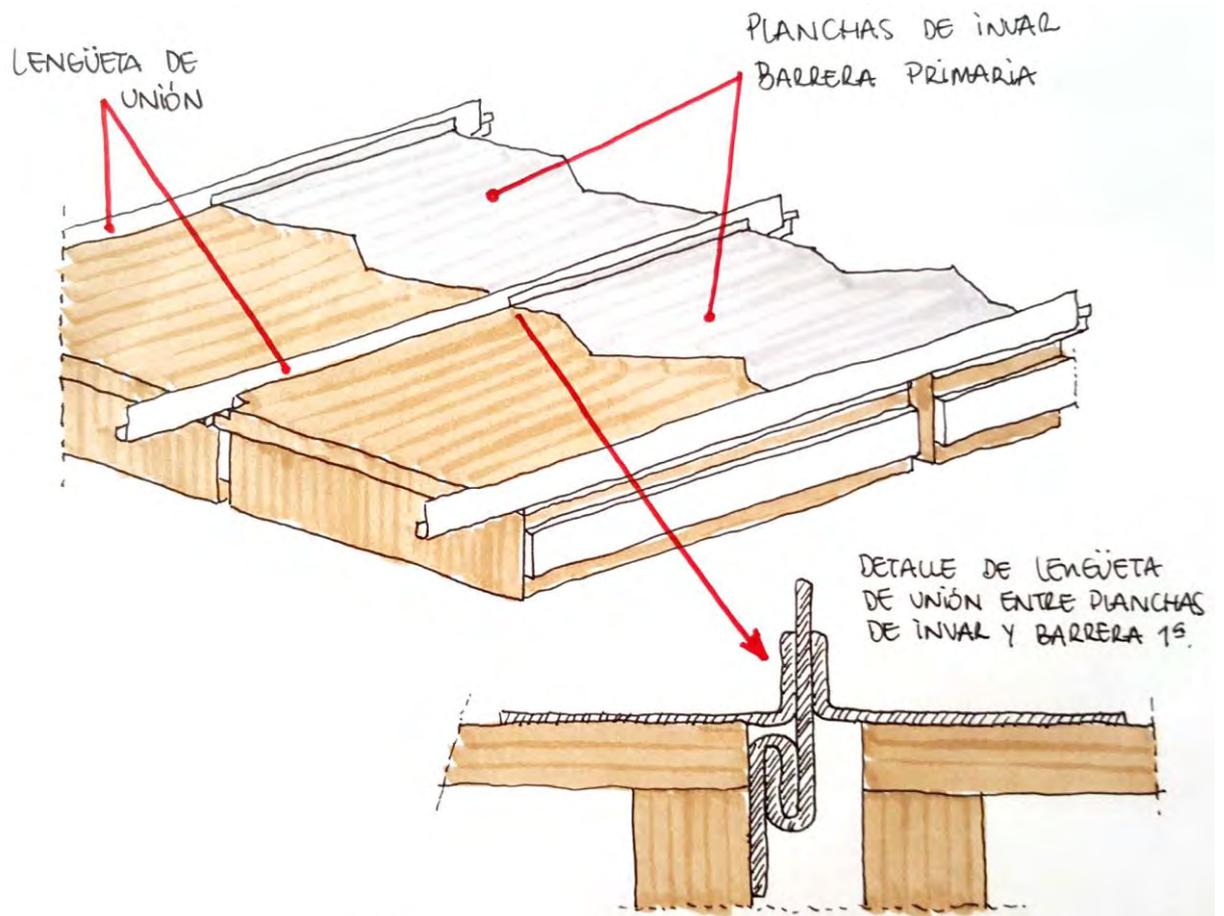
Unión de las cajas de madera a las planchas de Invar. Fuente: elaboración propia
